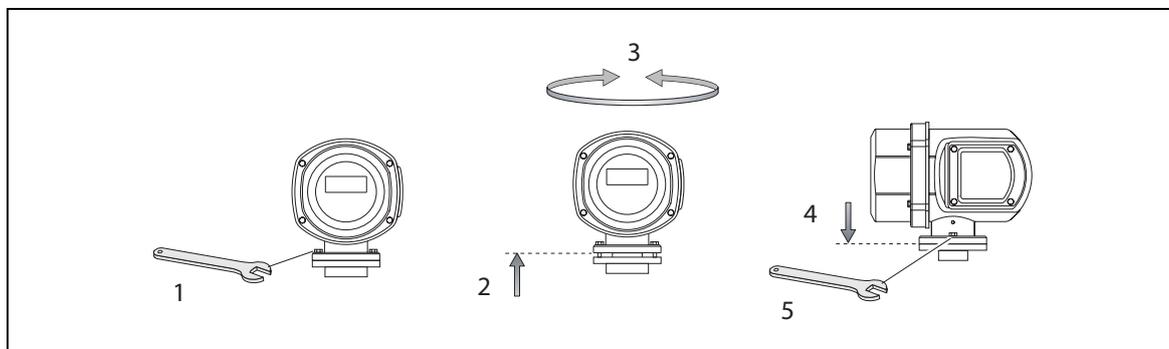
Поворот корпуса преобразователя (в рабочем корпусе из нержавеющей стали)
